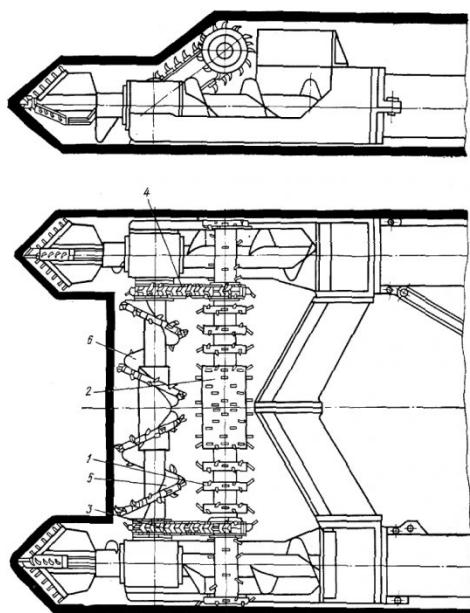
Исполнительный орган с дополнительным режущим устройством для отбойки верхней пачки угля:
